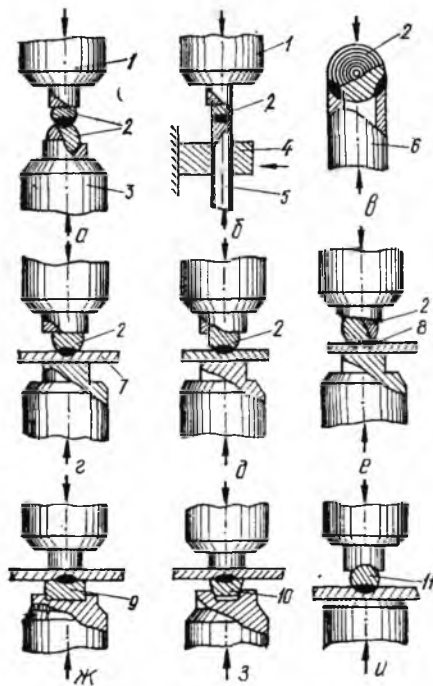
Схемы конденсаторной сварки шариков и контактов.
